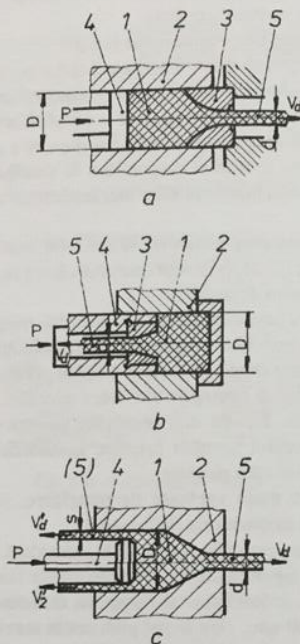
Scheme de principiu la extrudare: 1 - semifabricatul inițial; 2 - camera de presare; 3 - matrița; 4 - piston (poanson); 5 - piesa obținută prin extrudare; a - extrudare directă; b - extrudare indirectă; c - extrudare combinată.
